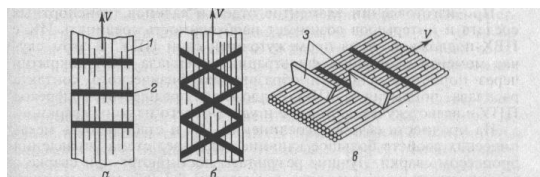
Схемы расположения сварных швов при изготовлении нетканых полотен (а, б) и схема расположения сварочных волноводов (в): 1 - волокнистый холст; 2 - сварной шов; 3 – волноводы
